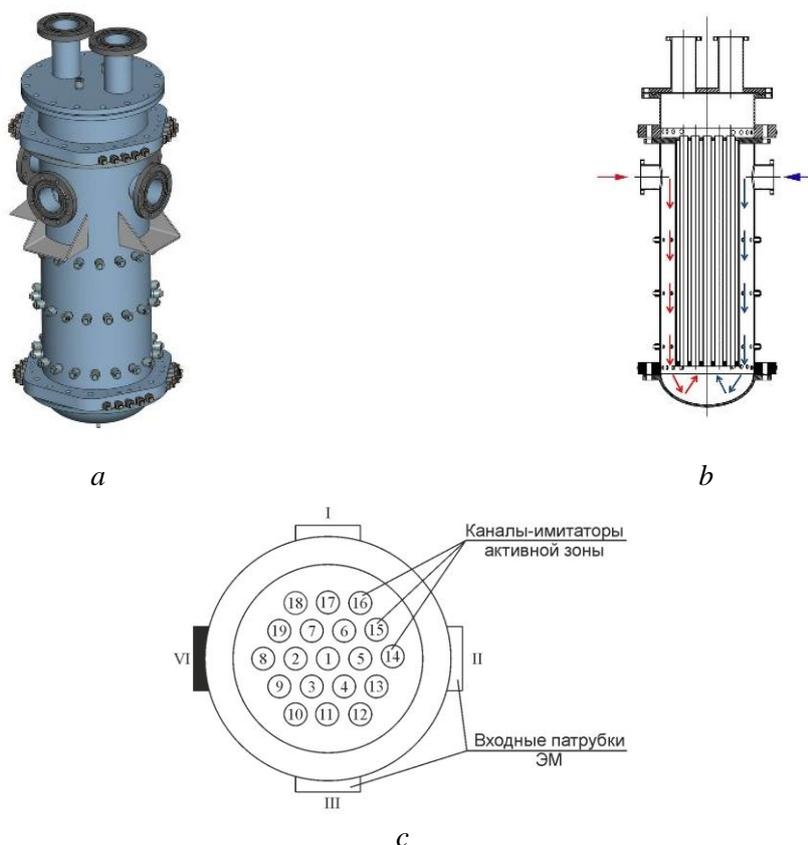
Экспериментальная модель напорной камеры ядерного реактора: а – общий вид; б – схема движения потоков; с – нумерация каналов-имитаторов активной зоны
